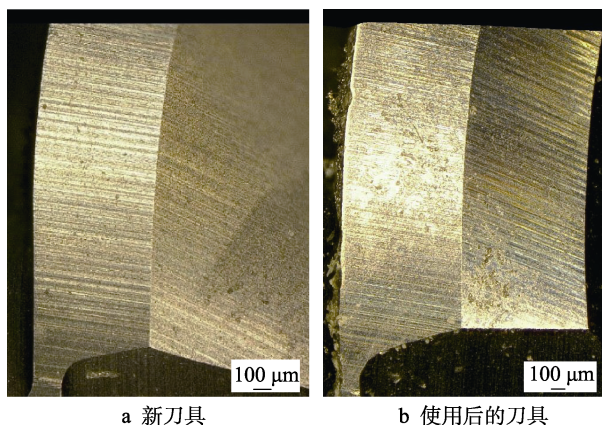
超声辅助铣削钛合金的刀具表面微观形貌
